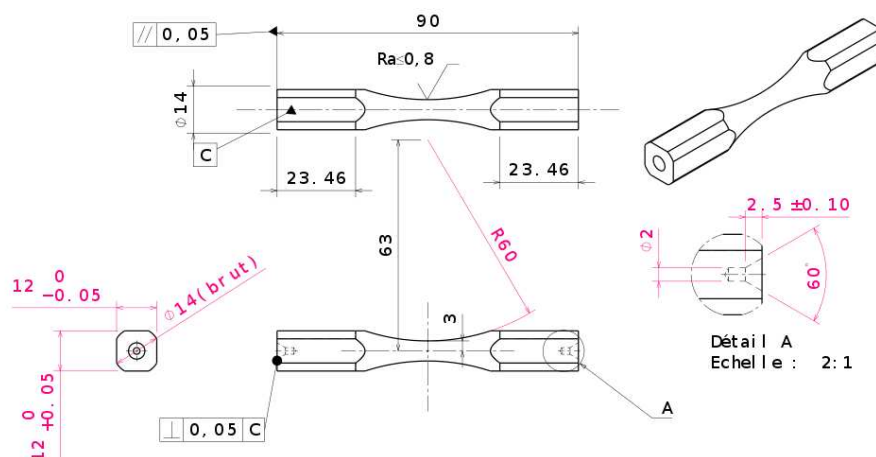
Géométrie des éprouvettes de fatigue en cuivre CuGS. L'axe longitudinal de l'éprouvette parallèle à la direction transversale DT (cf. figure 2.4)
